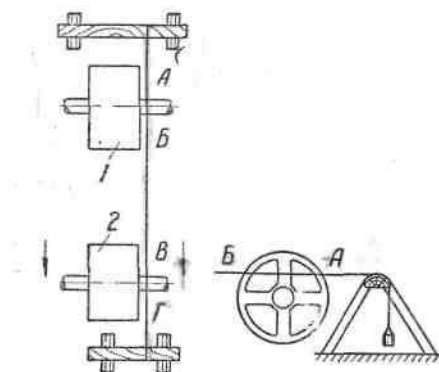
Проверка валов шнуром по шкивам: 1 — шкив установленного вала; 2 — шкив выверяемого вала
